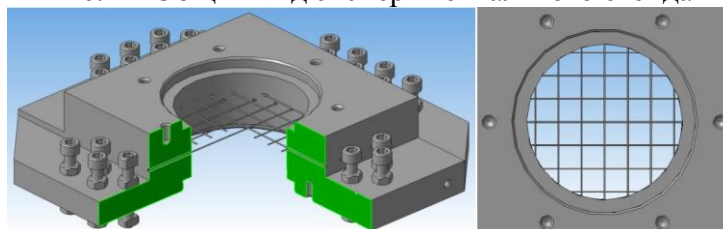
Конструкция сетчатого датчика (в разрезе и вид сверху)
